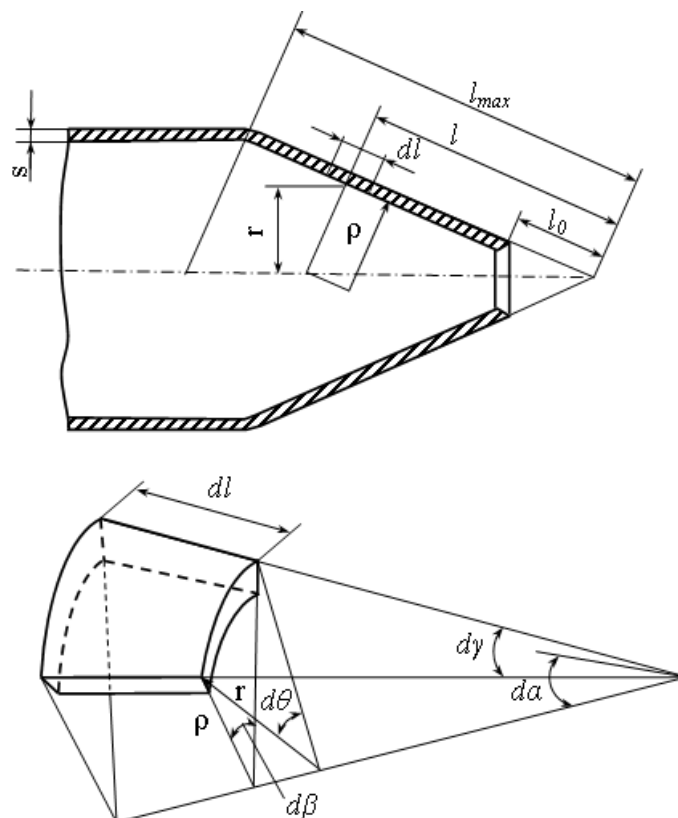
Схема до розрахунку НДС тонкостінної заготовки при обкочуванні
